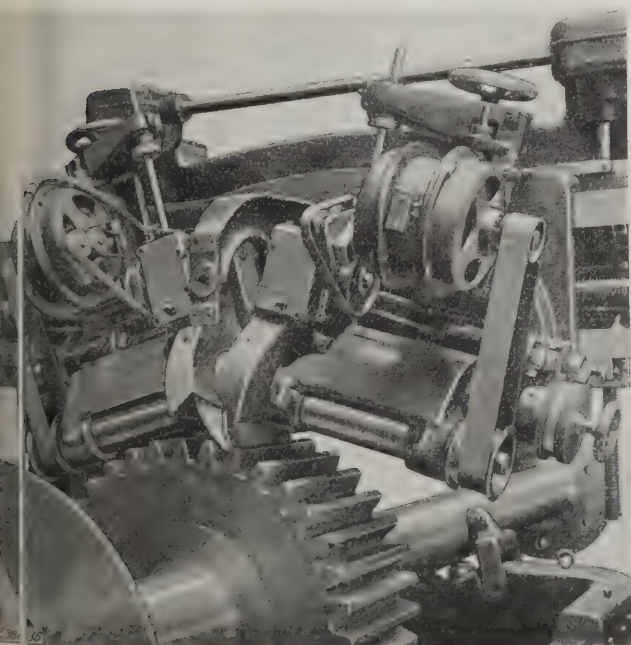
Die Schleifwerkzeuge der Zahnrad-Schleifmaschine von Maag.
